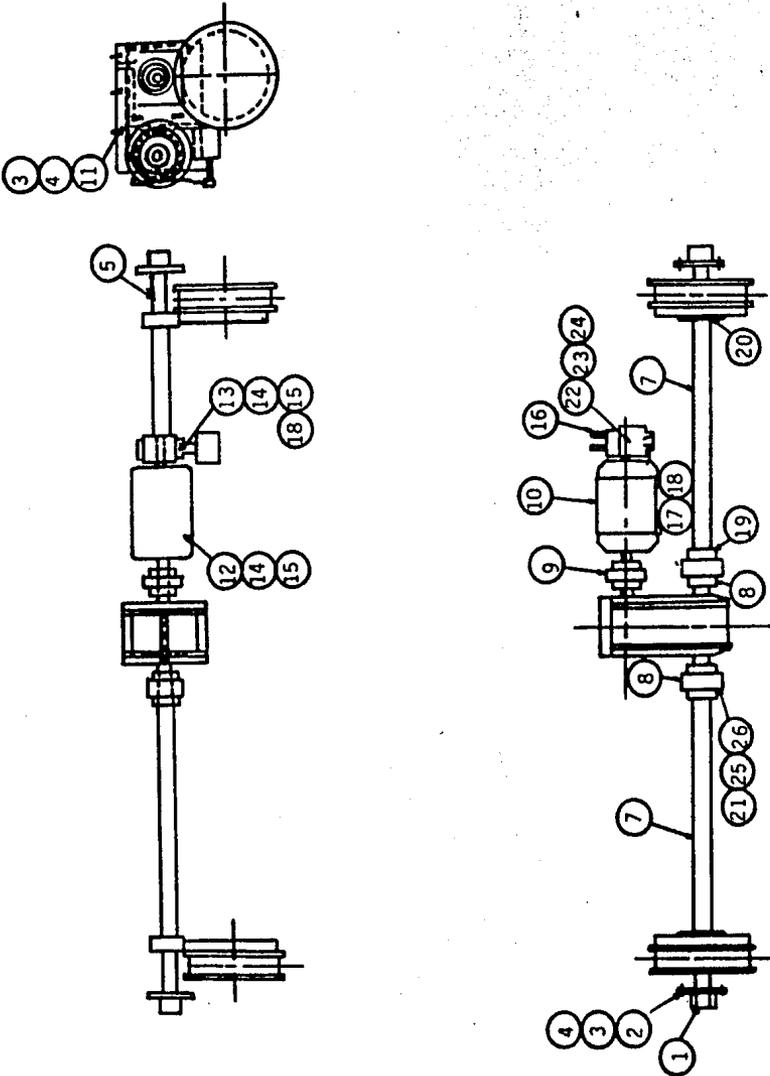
ENSAMBLE DEL MECANISMO DE DIRECCION
